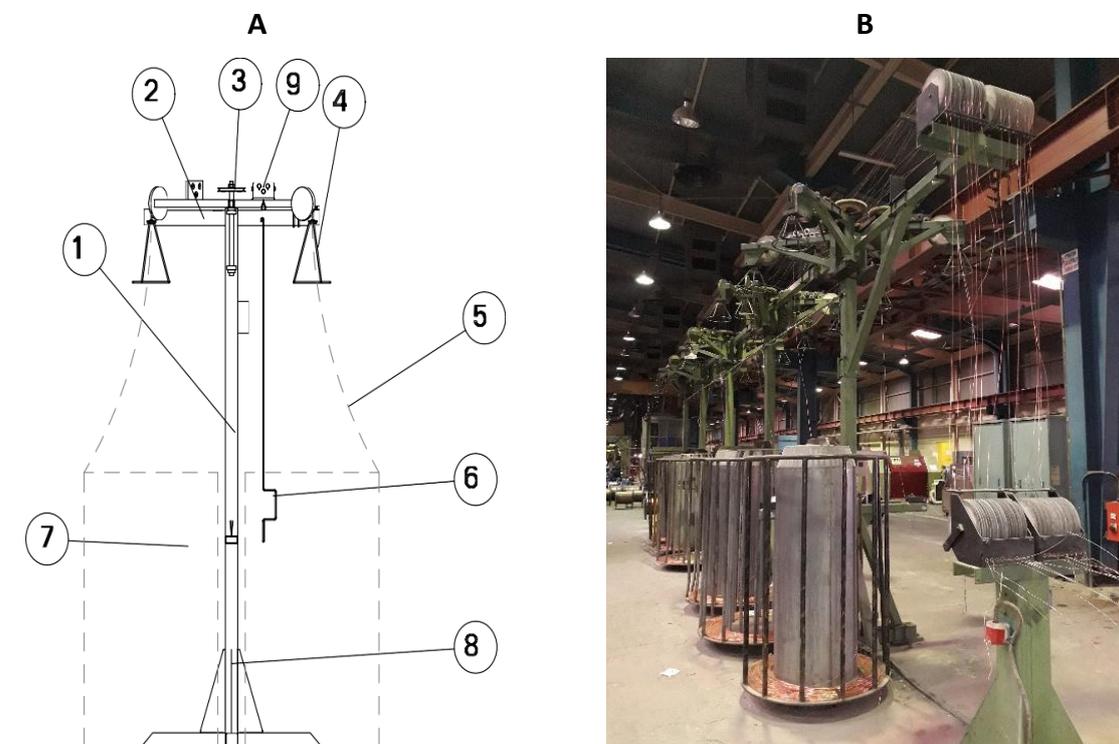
Éléments principaux de la machine(A) et vue réel (B)
